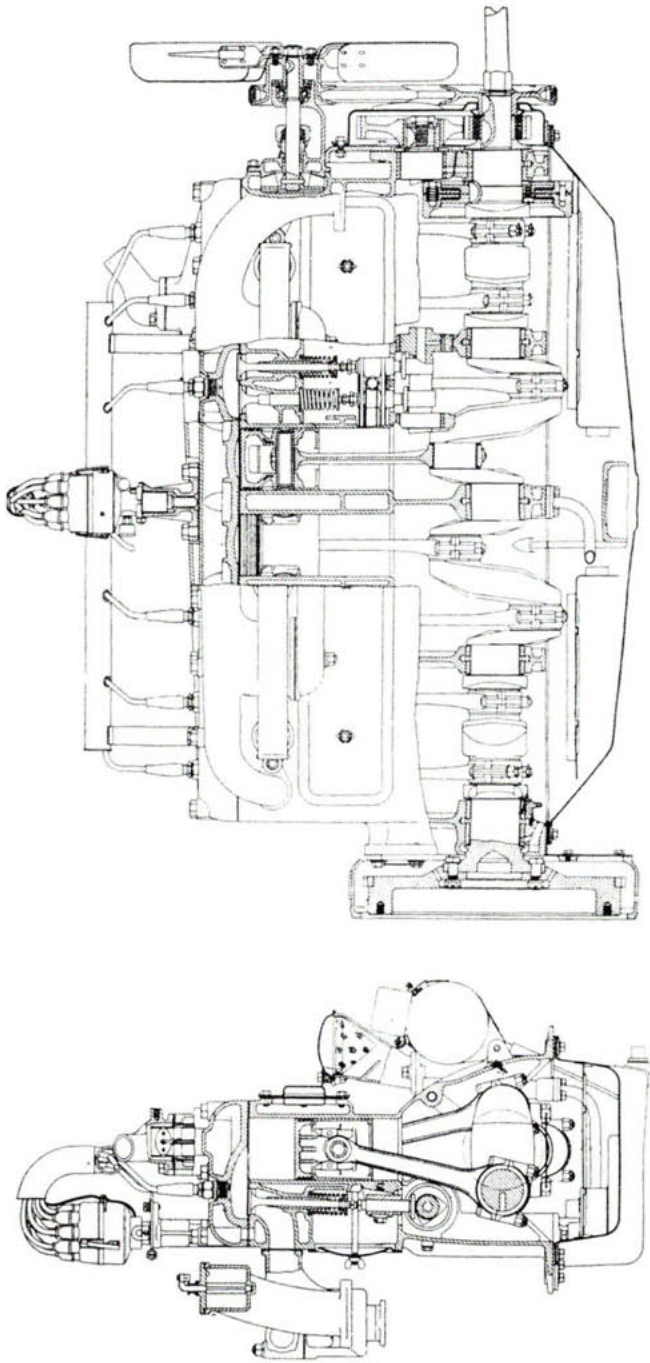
Längsschnitt und Querschnitt durch einen 8 Zyl.-Motor.
